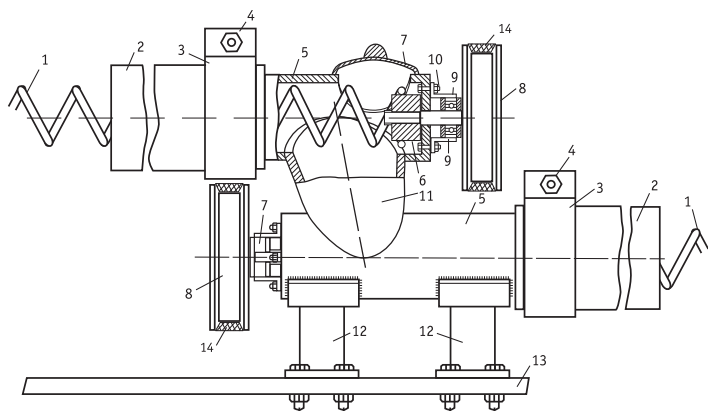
Деталь крепления спирали при перегрузке пылевидных материалов: 1 – спираль; 2 – шланг; 3 – хомут; 4 – болт; 5 – патрубок; 6 – хвостовик; 7 – ось шкива; 8 – шкив; 9 – подшипники; 10 – болт; 11 – отверстие; 12 – стойки; 13 – станина; 14 – ременная передача.
